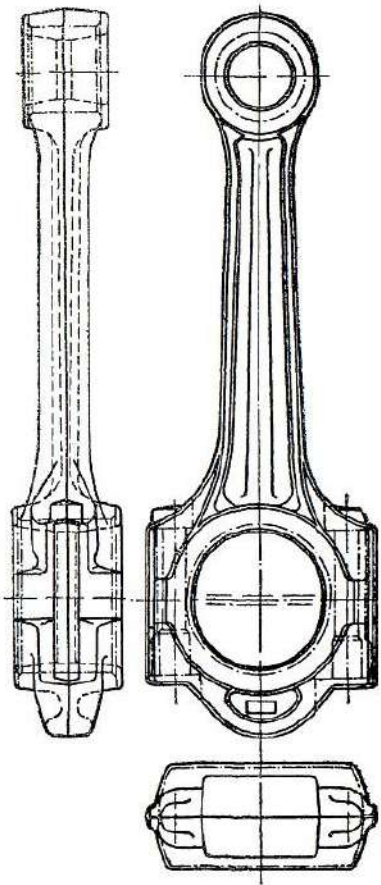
Заготовка шатуна, штампована заодно з кришкою
